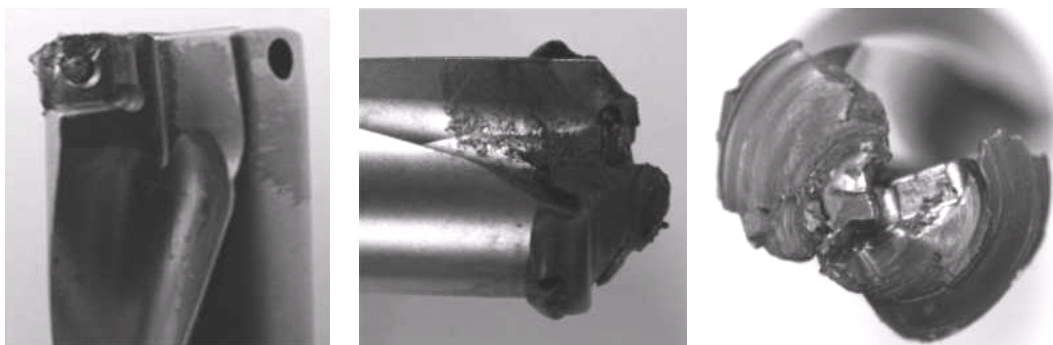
Результаты разрушений сборных сверл с режущими пластинами
